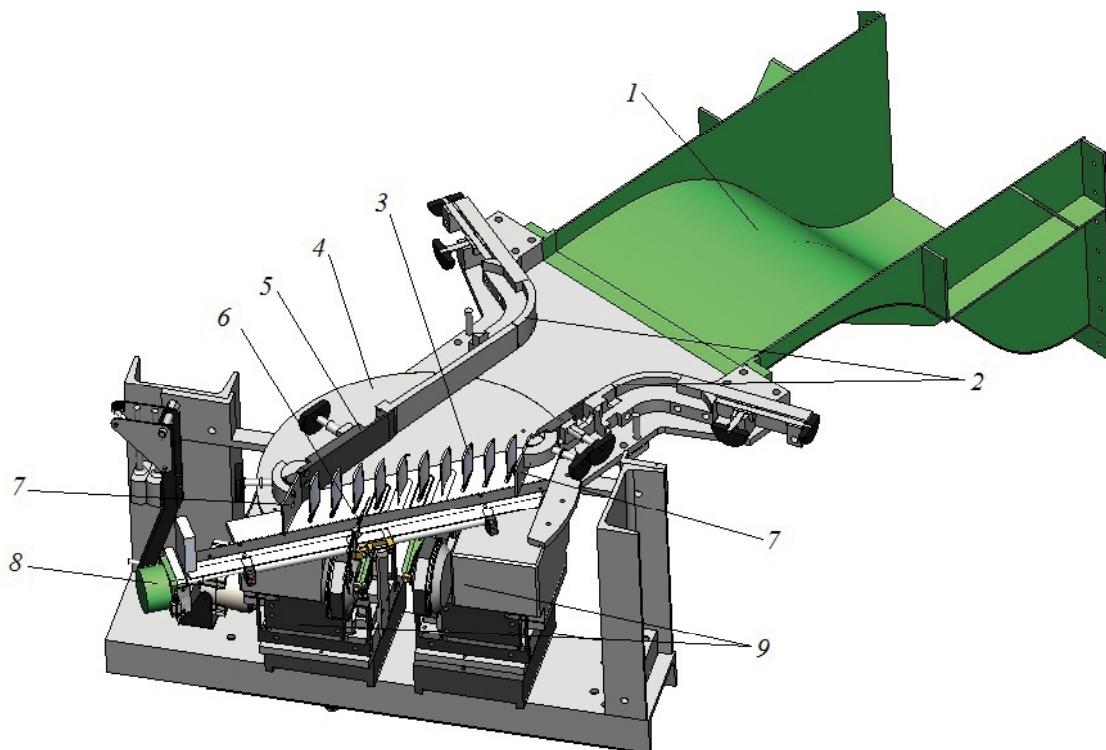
Разрез исходной конструкции рабочей части аэродинамического стенда
